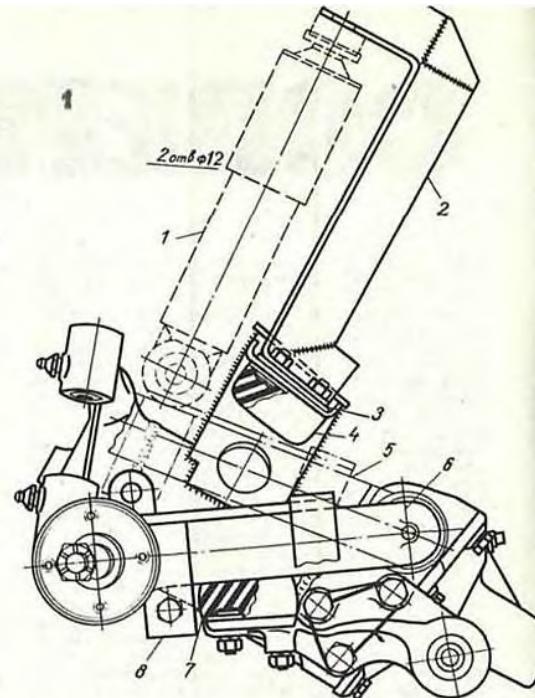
Общий вид установки передних телескопических амортизаторов «Москвича-402-407» на «Москвич-400 и 401»: 1 — амортизатор в сжатом состоянии; 2 — верхний кронштейн амортизатора; 3 — приваренная усиливательная пластина; 4 — отбойный резиновый буфер верхний; 5 — кривошип в верхнем положении (показан пунктиром); 6 — кривошип в нижнем положении; 7 — отбойный резиновый буфер нижний; 8 — нижний кронштейн амортизатора.
